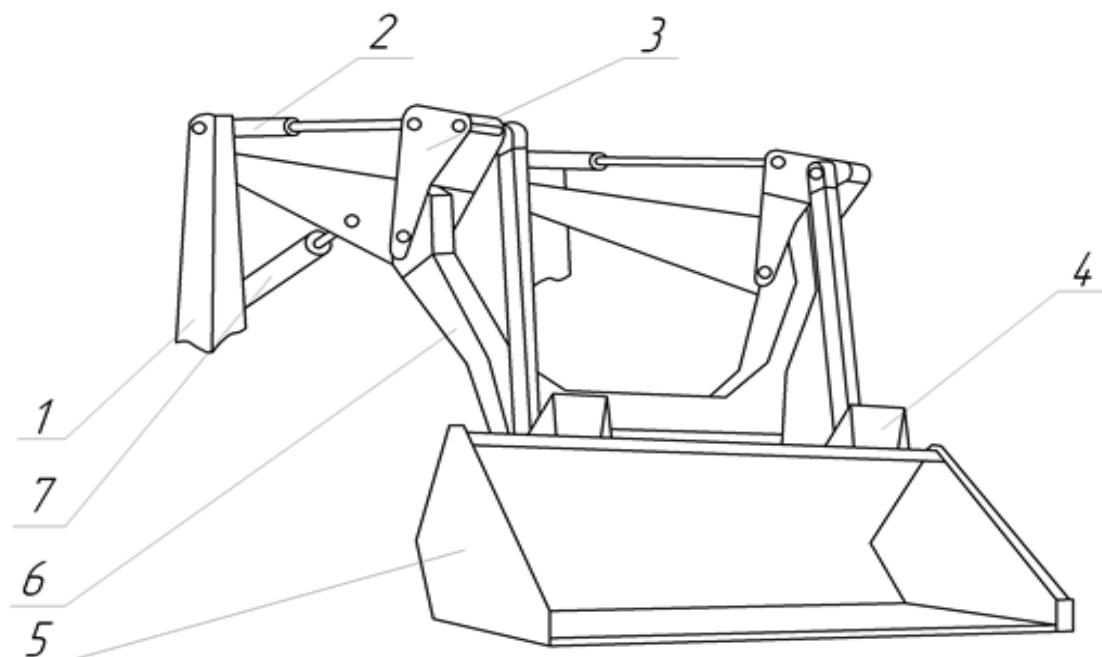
Рабочее оборудование УМП фирмы «GENL» (Германия): 1 – стойки крепления стрелы; 2 – гидроцилиндры управления ковшом; 3- механизм выравнивания положения ковша; 4 – суппорт с устройством для быстрой смены рабочего органа; 5 – ковш; 6 –стрела; 7 – гидроцилиндр подъема стрелы
